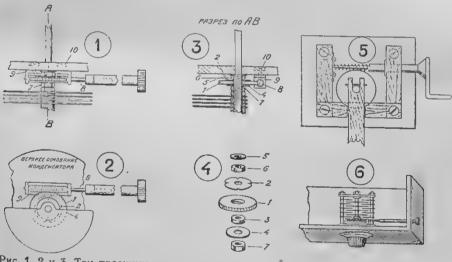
, 2 и 3. Три проекции червячного верньера, прикрепленного к конденсатору. Рис. 4. Детали для сборки. Рис. 5. Станок для нарезки зубчатого колеса. Рис. 6. Приемник с замонтированным конденсатором и укрепленным червячным , верньером.
